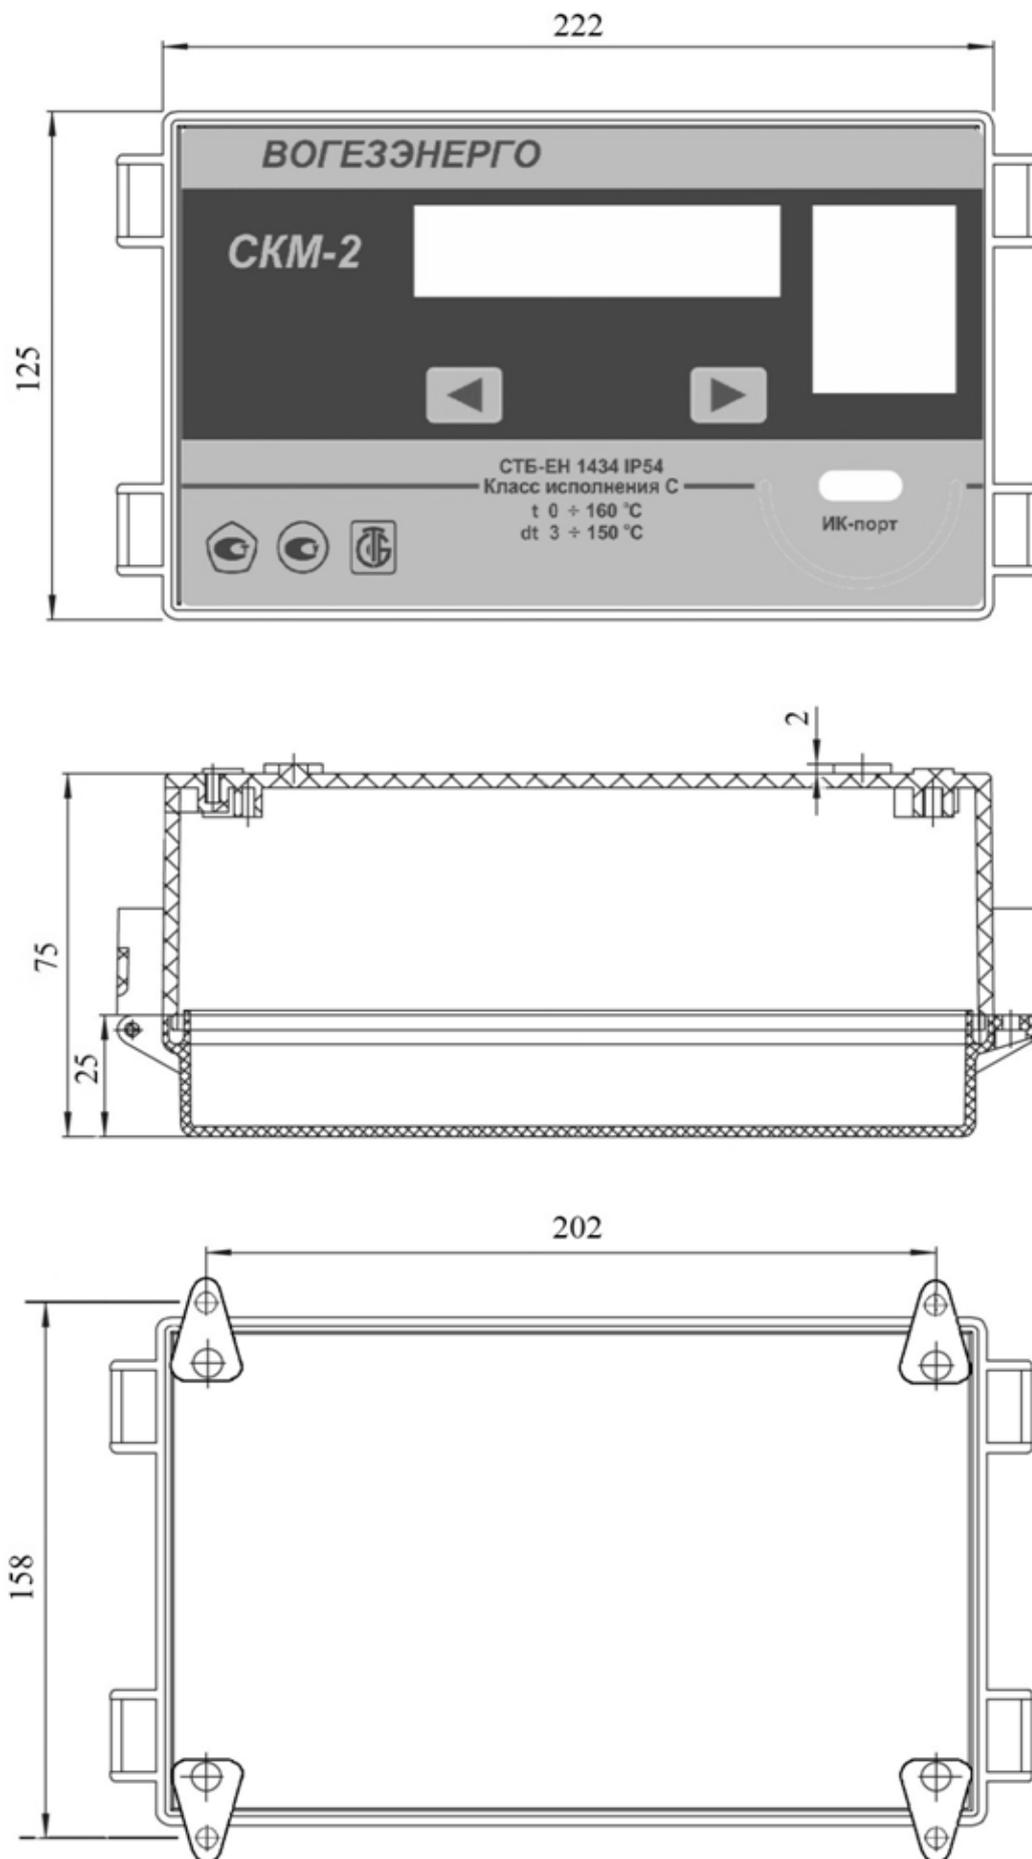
Габаритные и установочные размеры вычислителя многоканального (корпус Sanhe)
